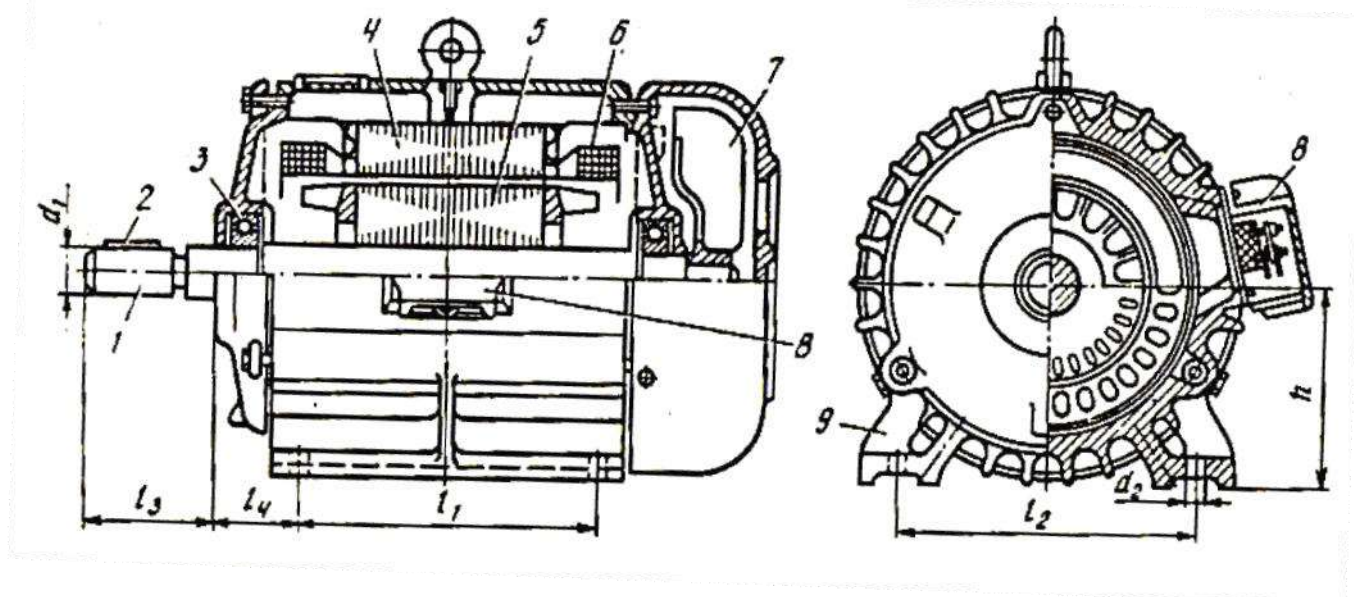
Устройство и установочные размеры электродвигателя серии 4А:
